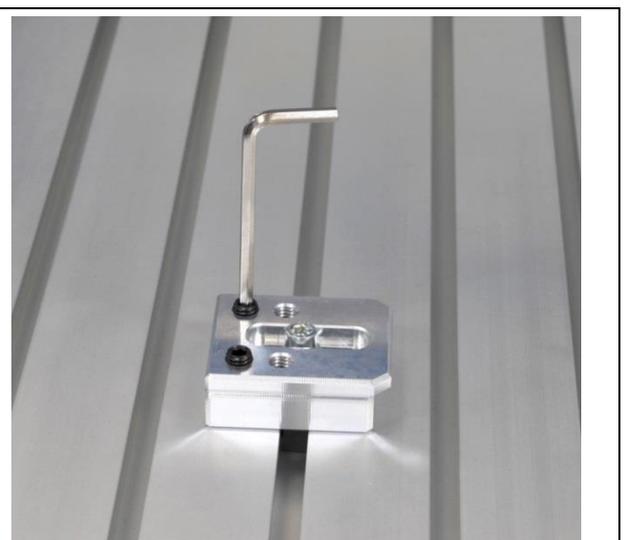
Höhe und Winkel der Spannpratze mittels Madenschrauben einstellen
